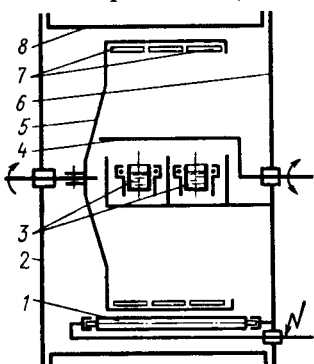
Внутрикамерное устройство установки с горизонтальной цилиндрической рабочей камерой:
